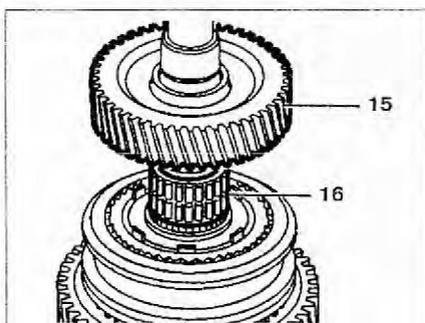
Снимите шестерню 15 2-й передачи и игольчатый подшипник 16.
